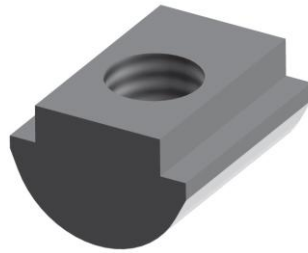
Eslabón de unión (ASS AUTOMATION-SYSTEME, 2014)
